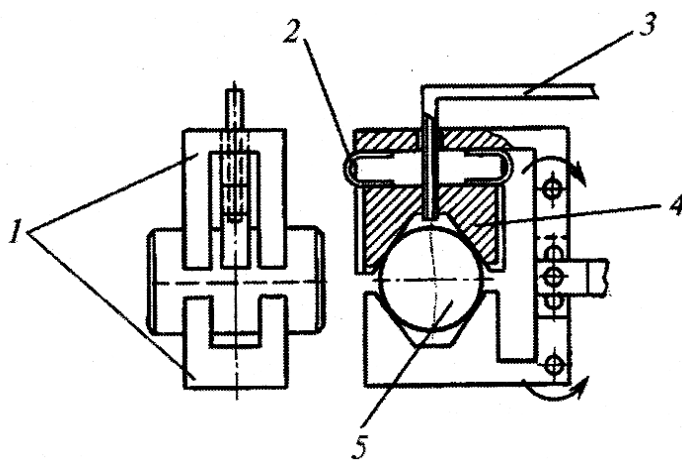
ЗП з пристроєм для виміру обробленої деталі:
